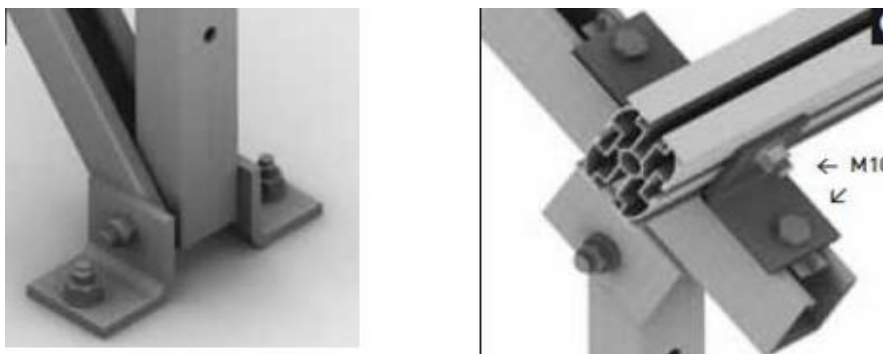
Estruturas transversais Standard tipo 2 e Light tipo 2.
